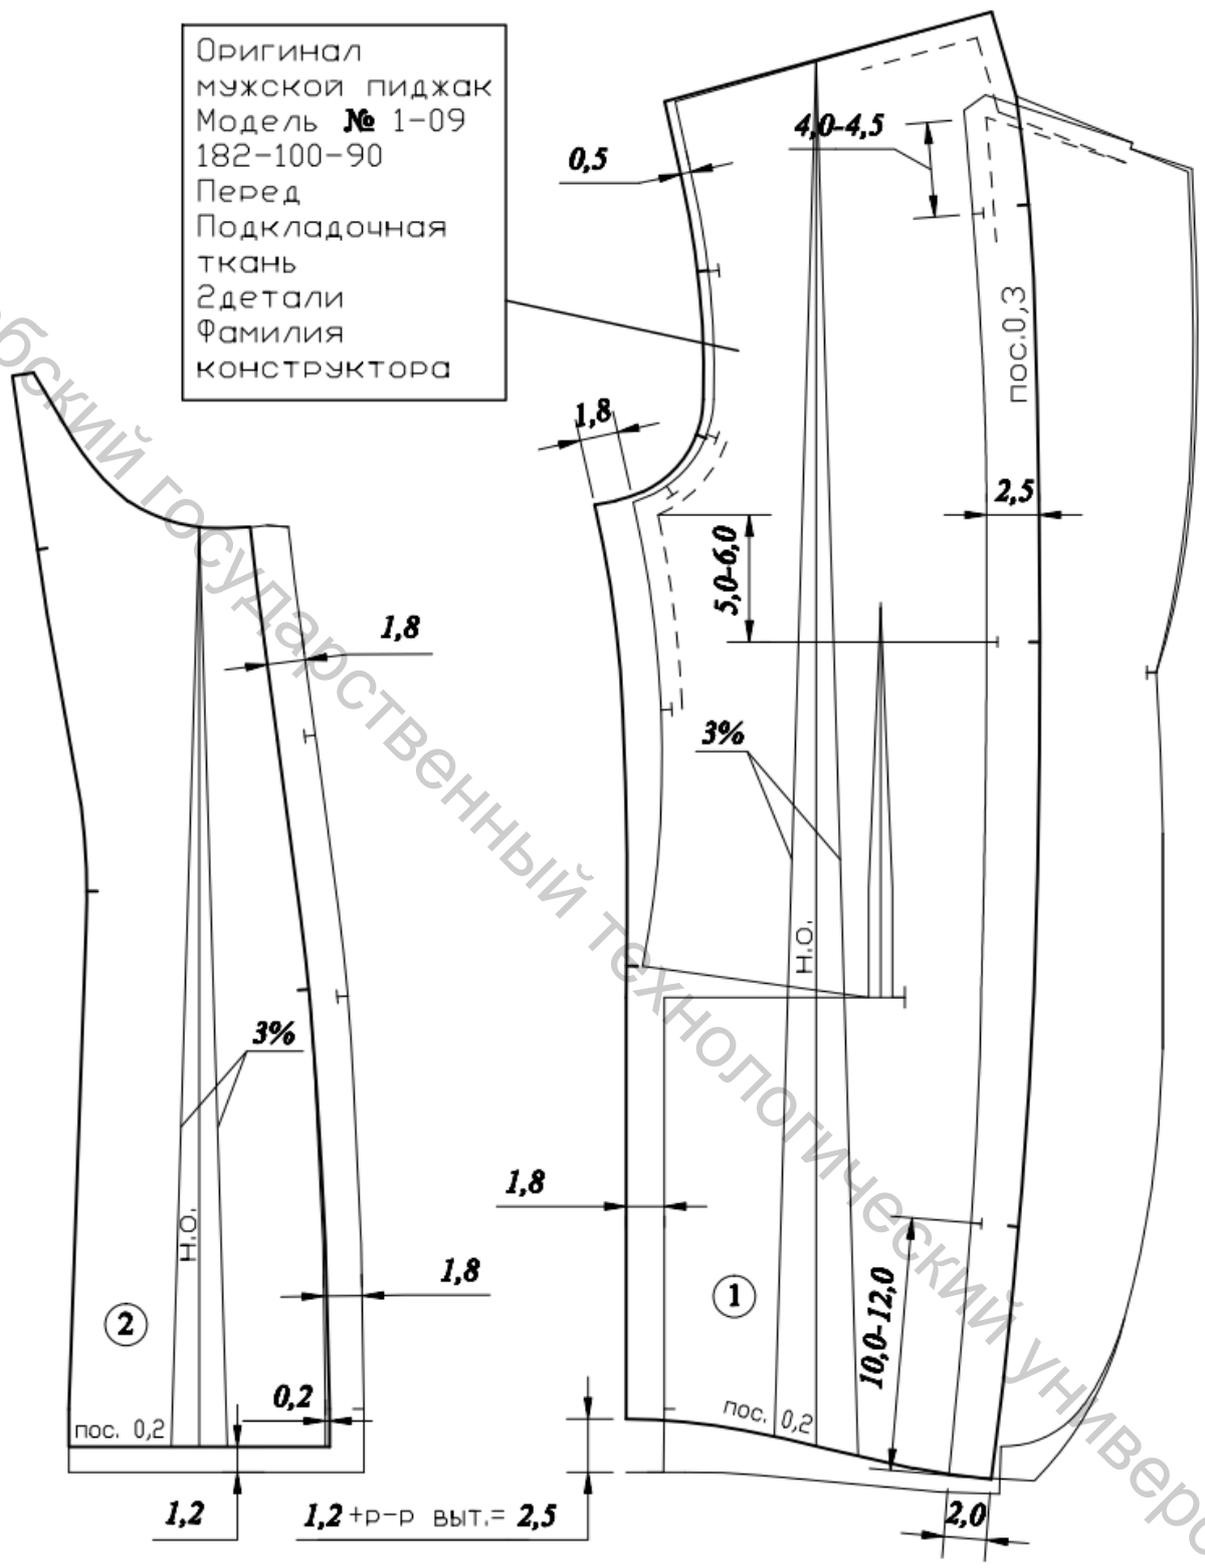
Схема построения чертежей лекал деталей переда и бочка мужского пиджака из подкладочной ткани
